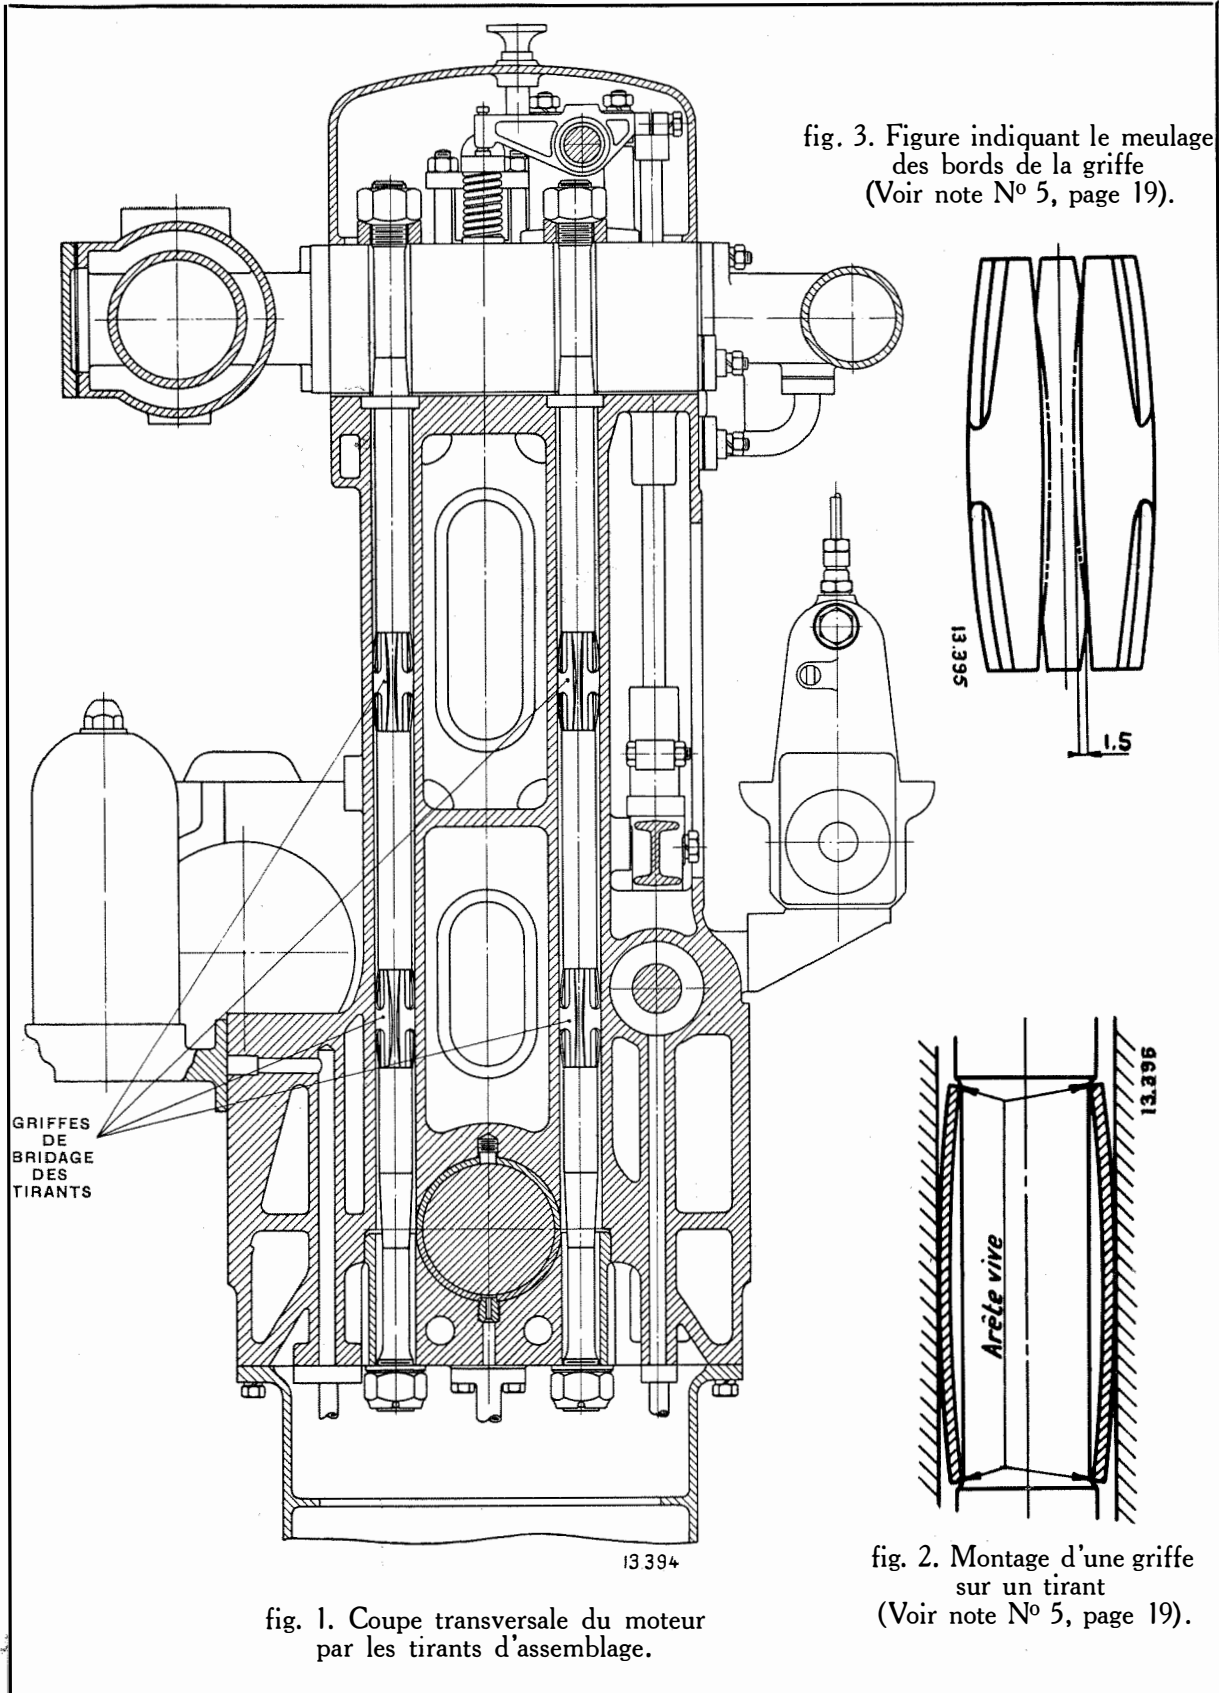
Coupe transversale du moteur par les tirants d'assemblage.
